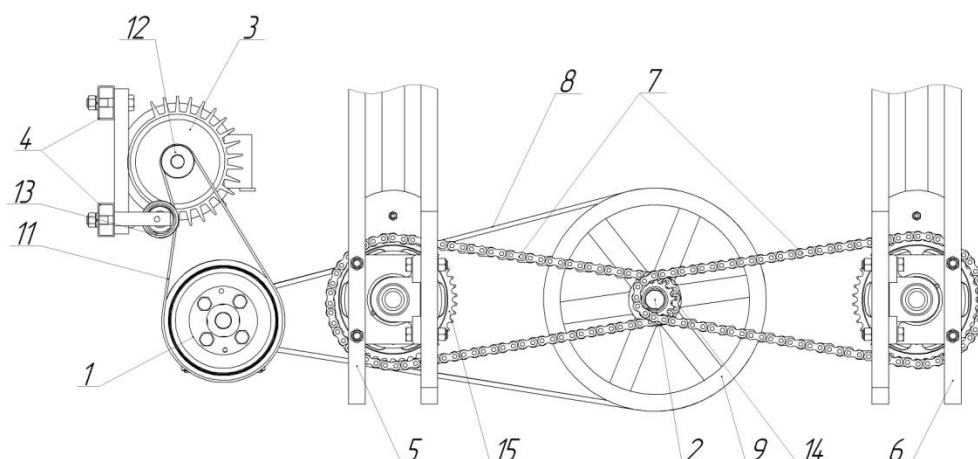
Компоновка привода стенда вид сбоку и сверху
